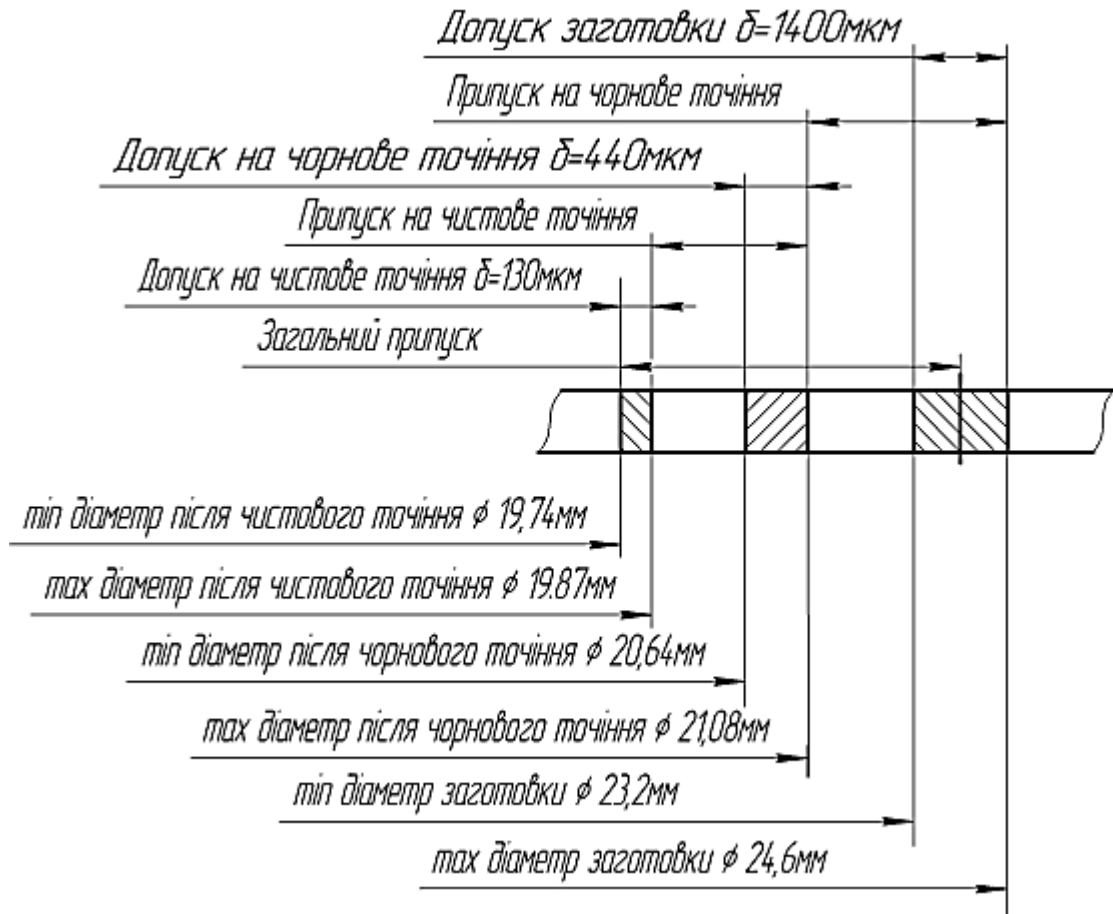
Схема розташування полів допусків і припусків на обробку поверхні розміром $\varnothing 20c11_{-0,24}^{-0,11}$
